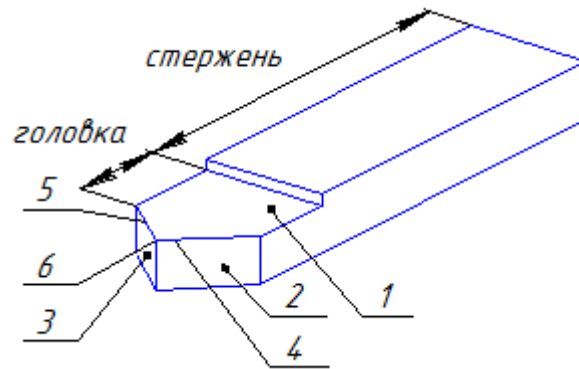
Строение проходного резца: 1 – передняя поверхность, 2 – главная задняя поверхность, 3 – вспомогательная задняя поверхность, 4 – главное режущее лезвие, 5 – вспомогательное режущее лезвие, 6 – вершина резца
